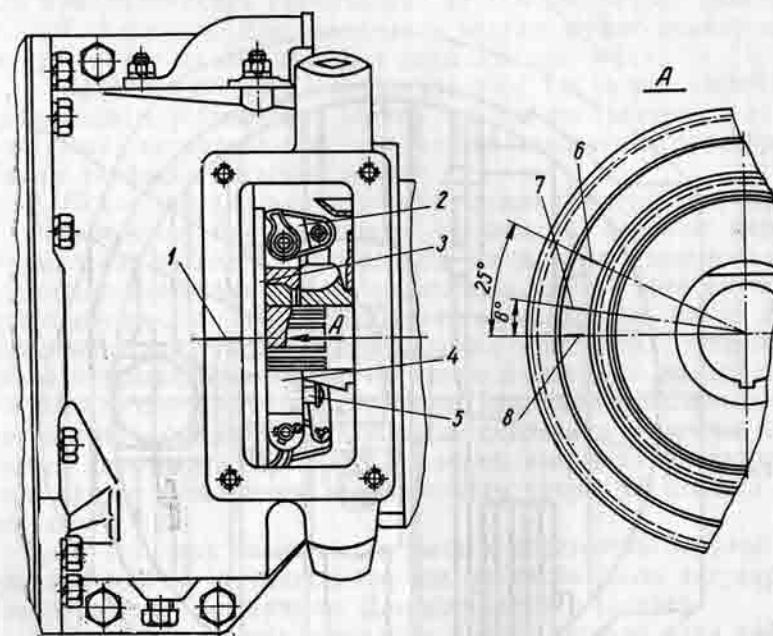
Регулировка муфты сцепления и совмещение рисок на корпусе муфты сцепления и маховике пускового двигателя:
